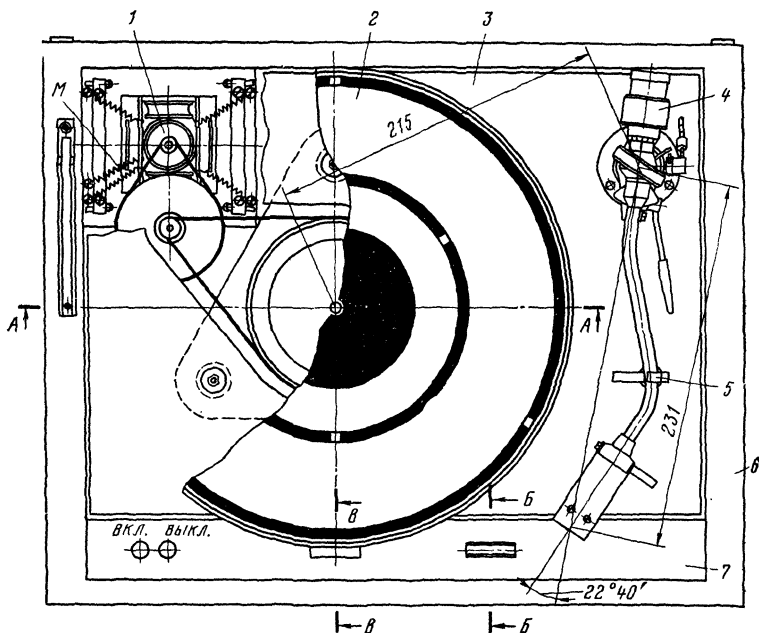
Конструкция проигрывателя (вид сверху, крышка не показана, нумерация деталей соответствует нумерации на рис. 75).
